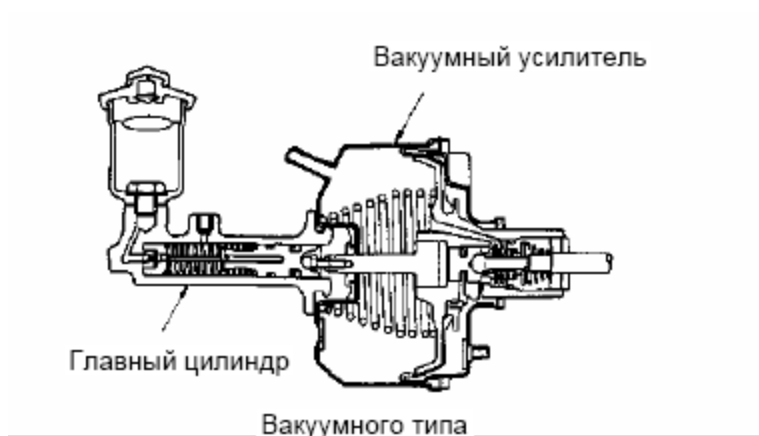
Вакуумный усилитель гидравлического привода сцепления
